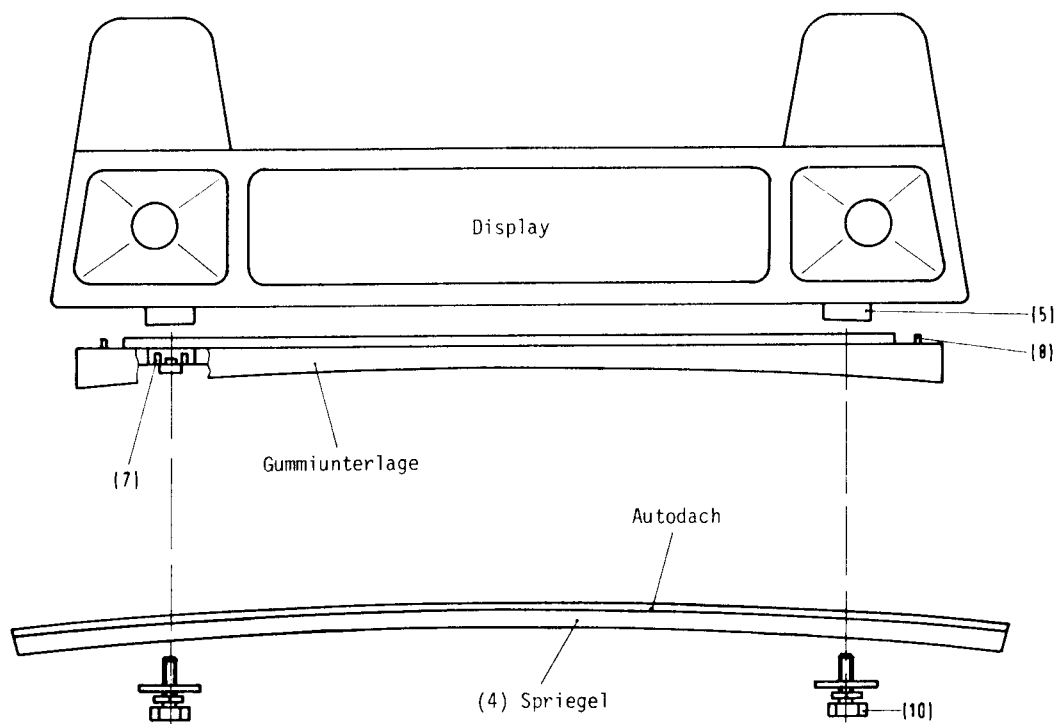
Frontansicht TOP-2/Fahrzeugdach (VW)
